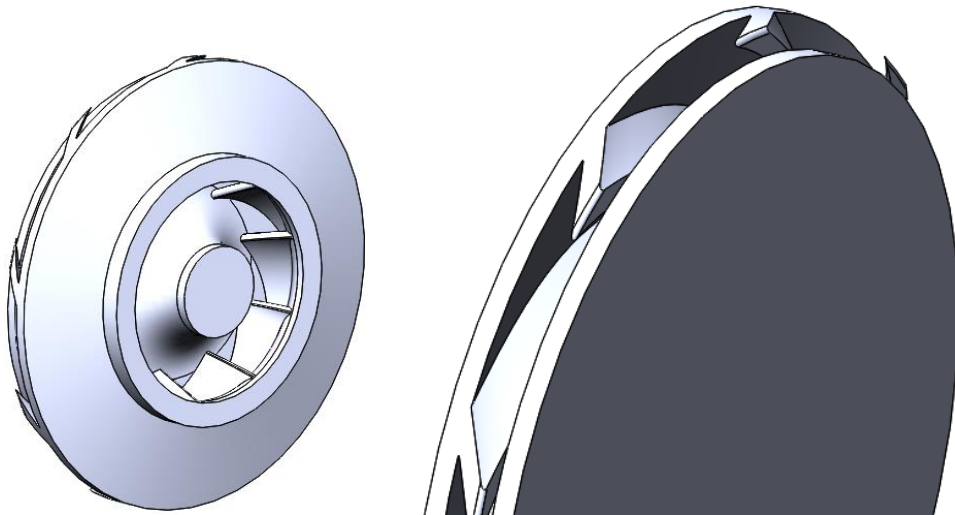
Общий вид рабочего колеса по второй схеме
